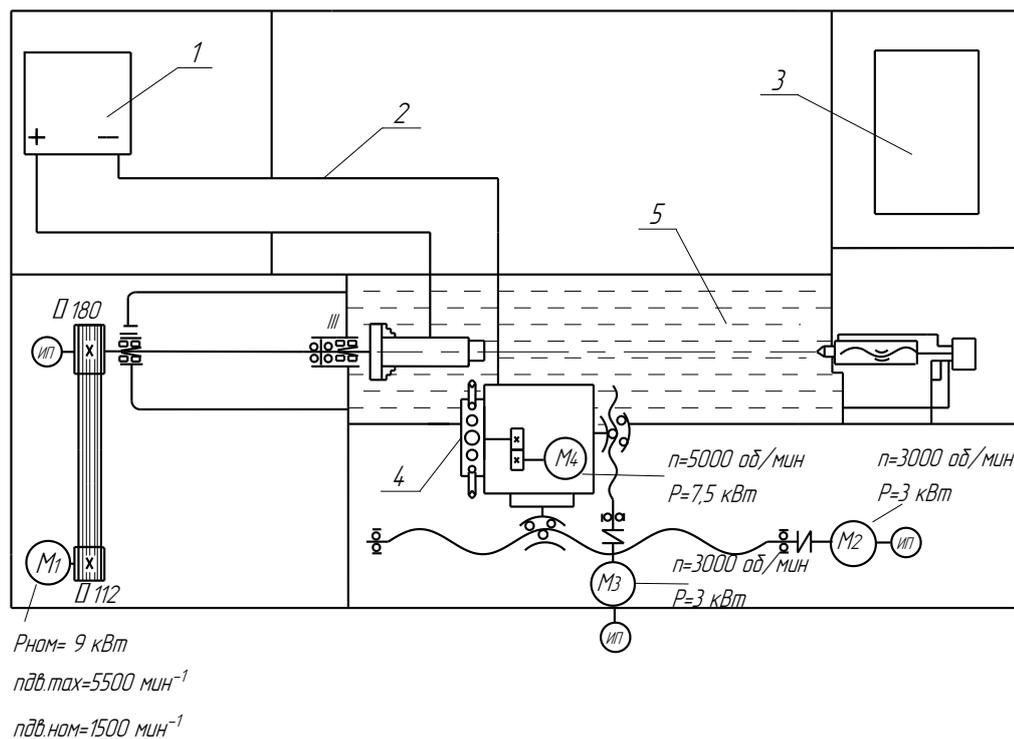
Кинематическая схема бироторного обрабатывающего комплекса.
